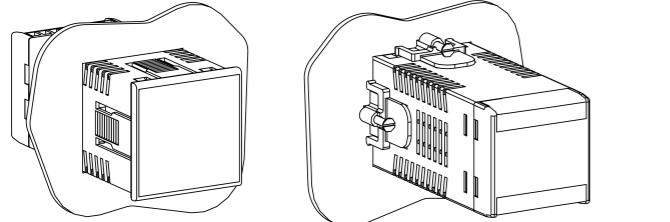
Монтаж прибора щитового крепления Щ5
